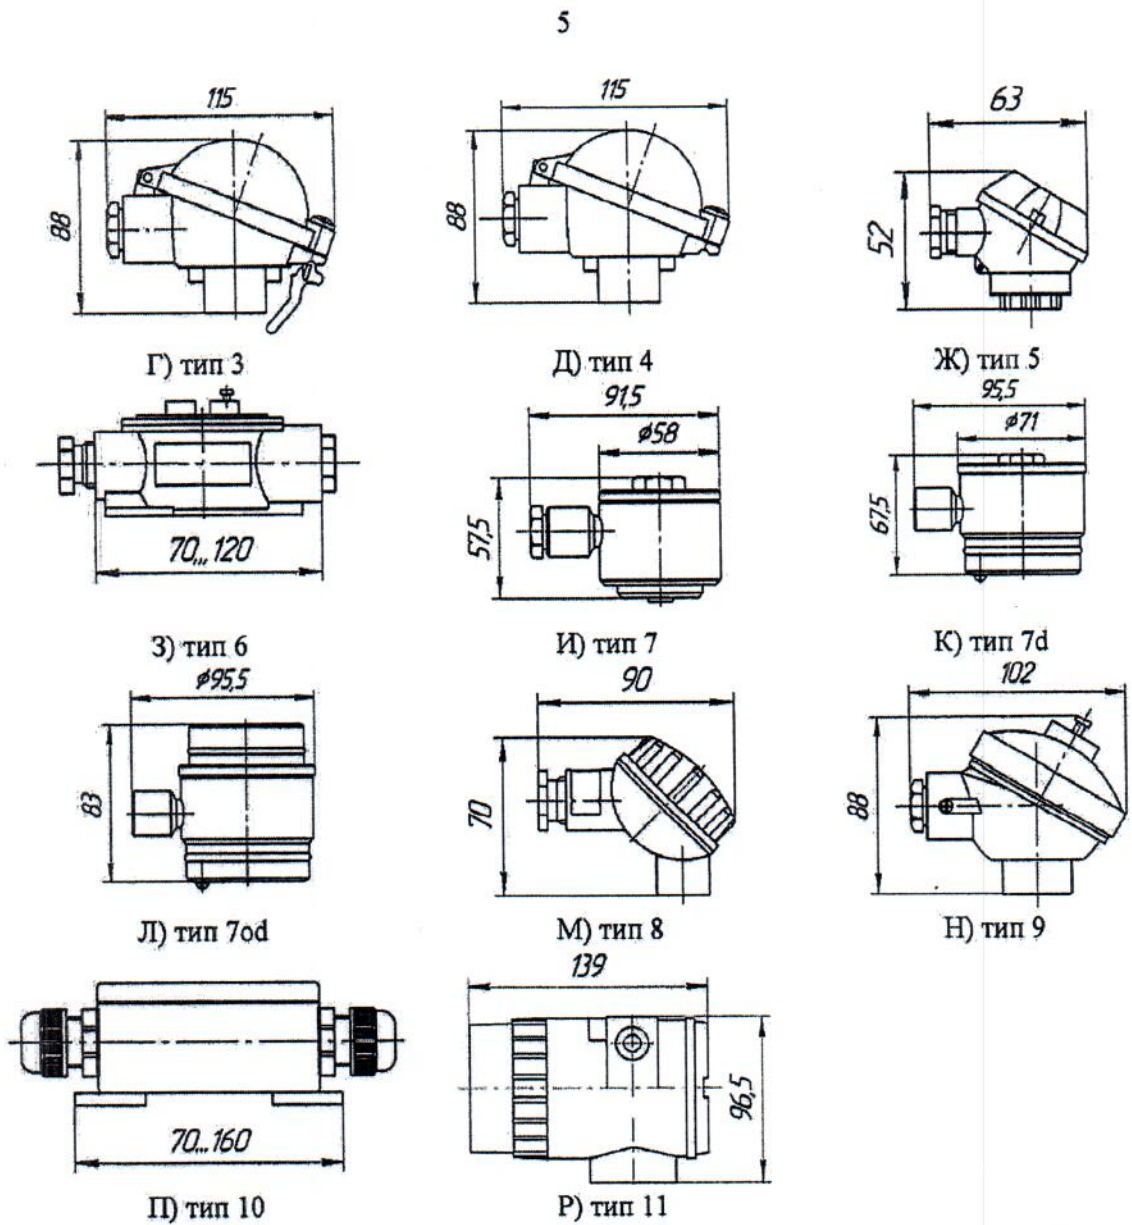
Чертежи внешнего вида конструктивного исполнения корпусов ТП
